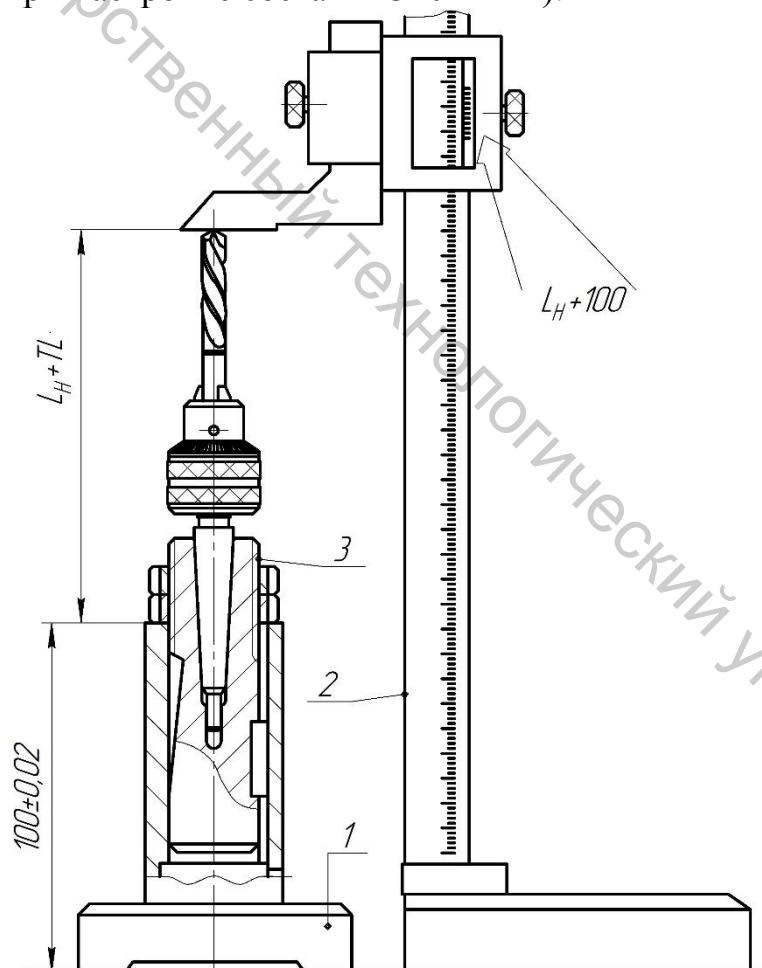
Схема настройки вне станка сверла на наладочные размеры: 1 – стойка, имитирующая шпиндель; 2 – штангенрейсмас; 3 – регулируемая втулка
